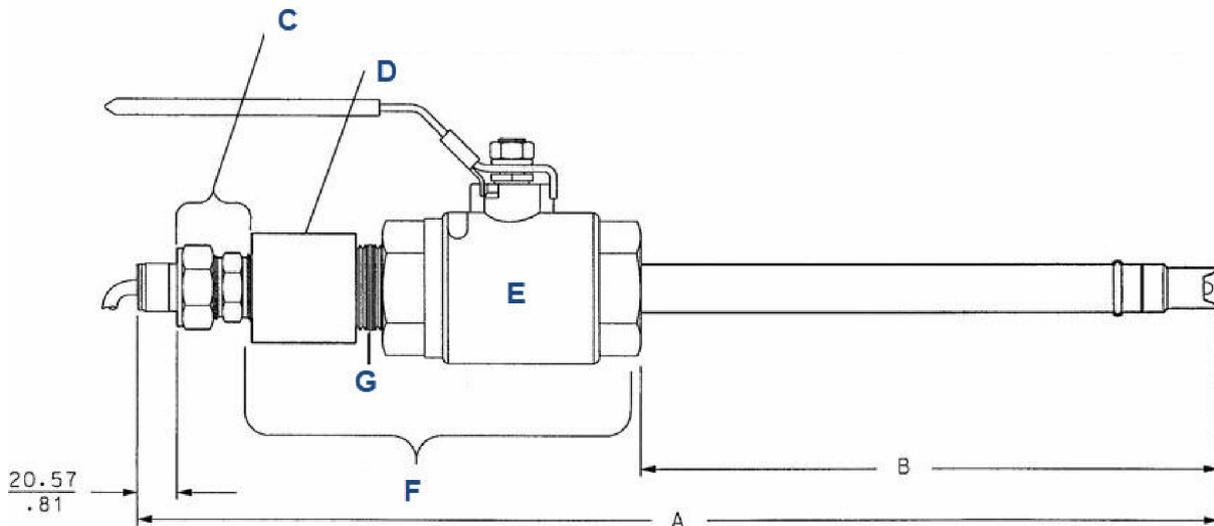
Габаритный чертеж Rosemount 396P/396PVP
